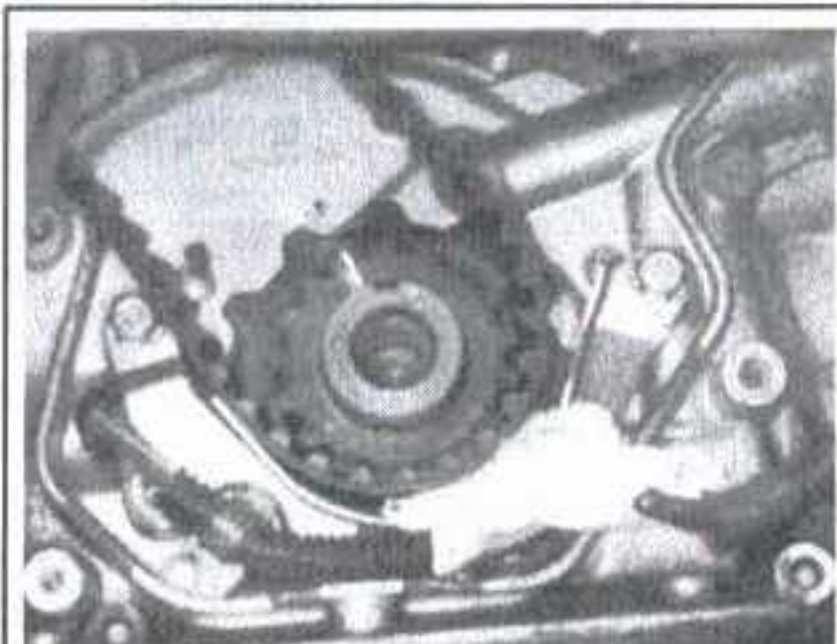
Датчик СКФ расположен под нижней крышкой ремня привода ГРМ за шкивом коленвала. Для контроля за частотой оборотов коленвала используется большое зубчатое колесо
